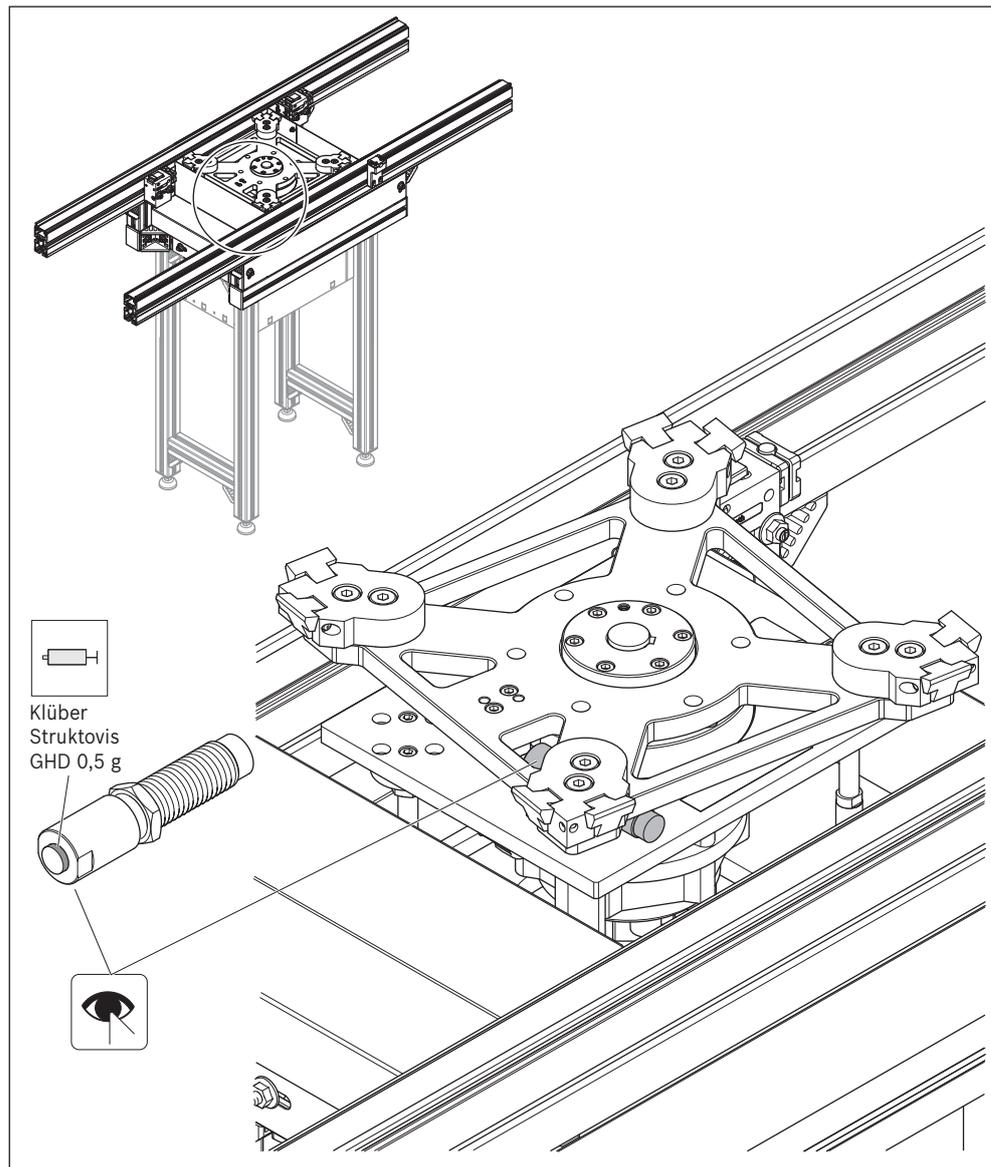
Bolzenvorlagerung der Dämpfer schmieren
